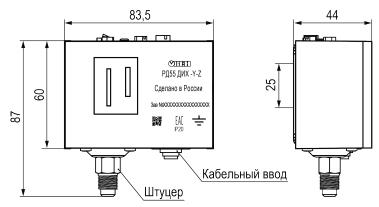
Габаритные и присоединительные размеры прибора
